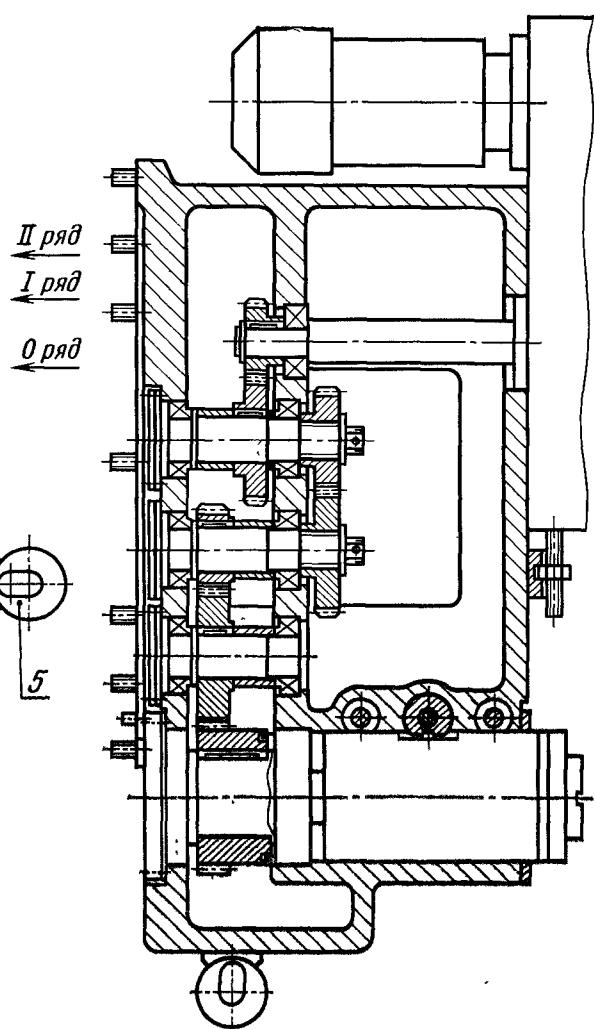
Вариант компоновки фрезерной бабки вертикального исполнения
